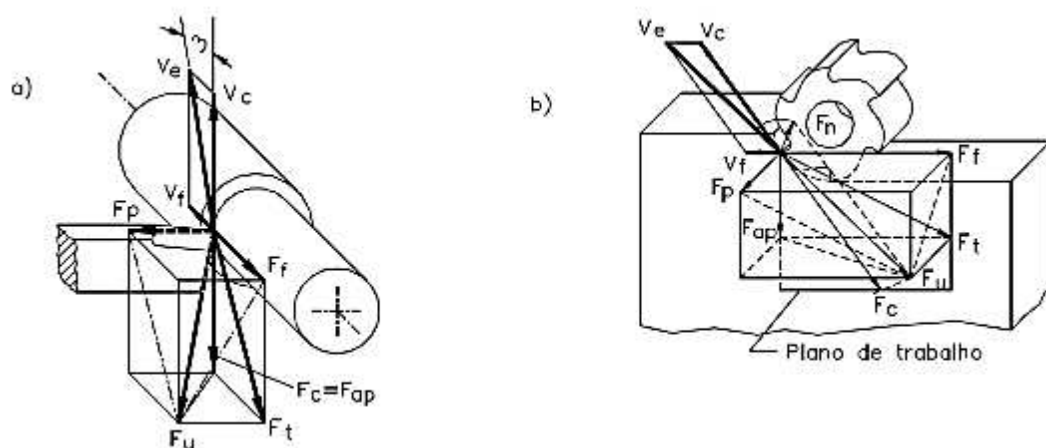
Componentes da Força de Usinagem. a) no torneamento; b) no fresamento (MACHADO et al., 2004).
